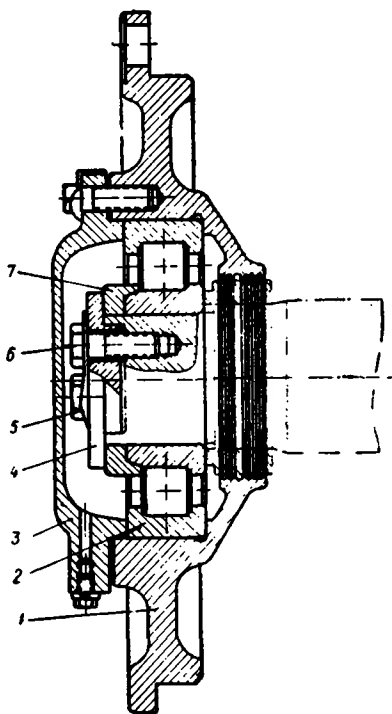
Подшипниковый щит тягового двигателя ДК-304Б с роликовым подшипником № 62417:
